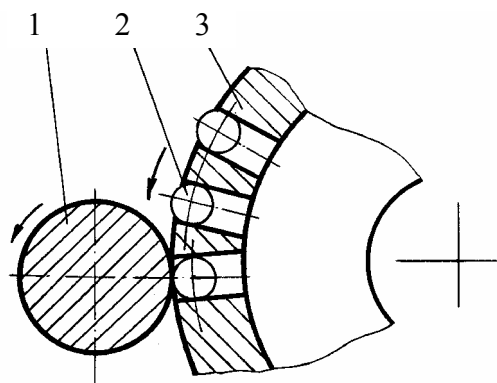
Схема устройства для ротационного упрочнения: 1 – деталь; 2 – шарики; 3 – корпус
